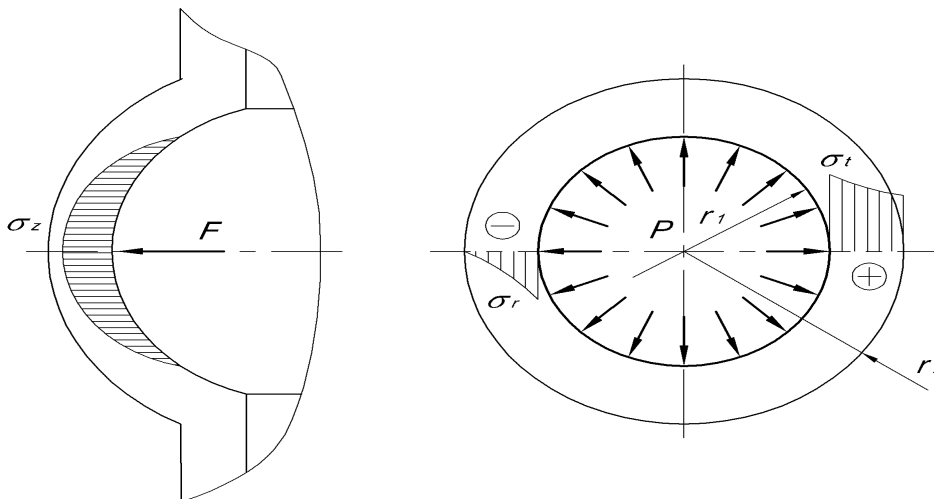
Схема дії сил і напружень при розвальцюванні циліндричної втулки
